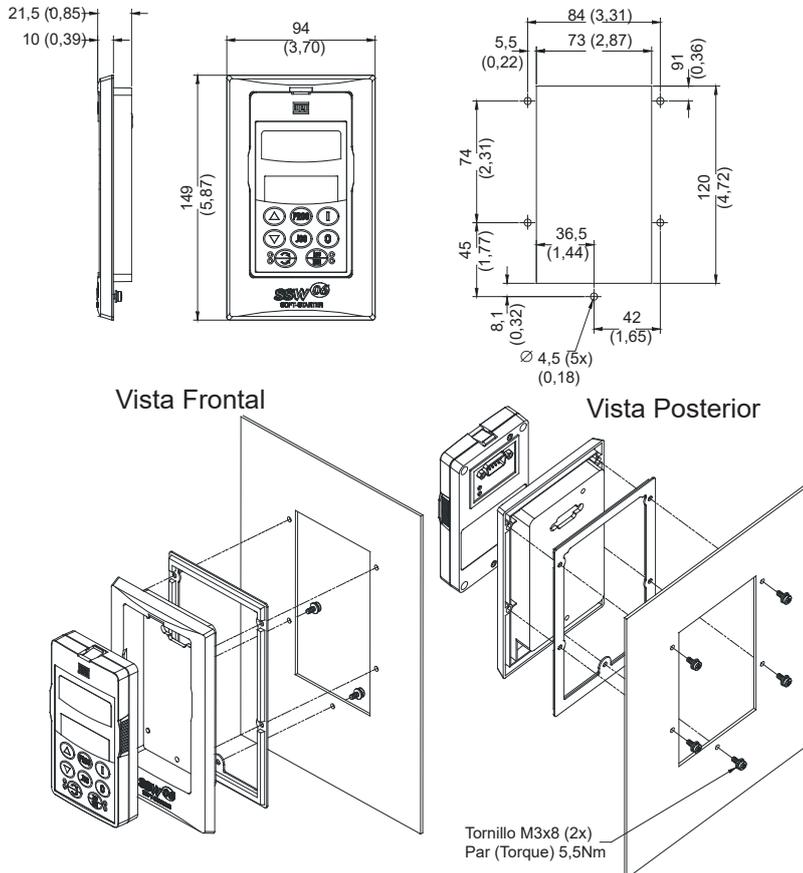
Dimensiones en mm (in) y instalación de la HMI y moldura en el panel
